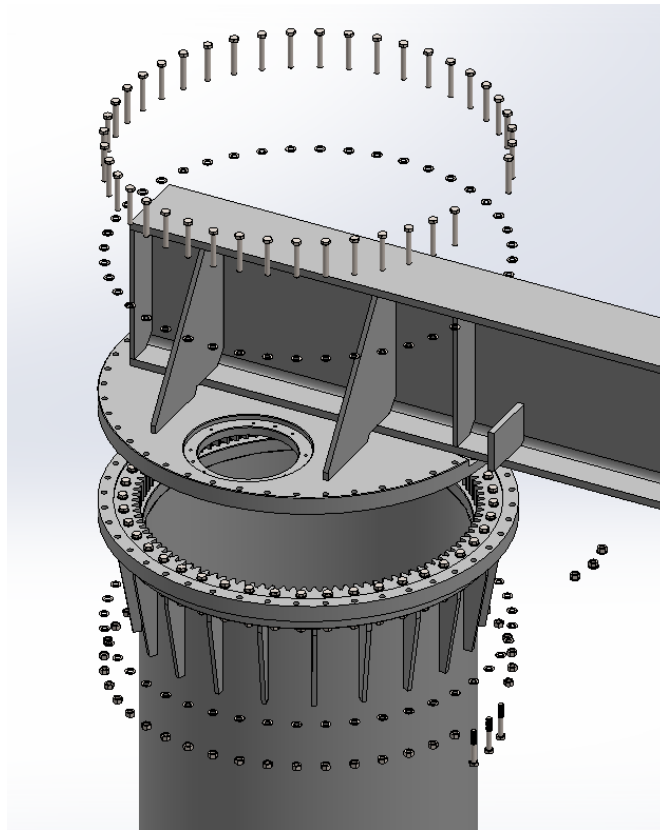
Vista explosionada del montaje del conjunto de la pluma.
